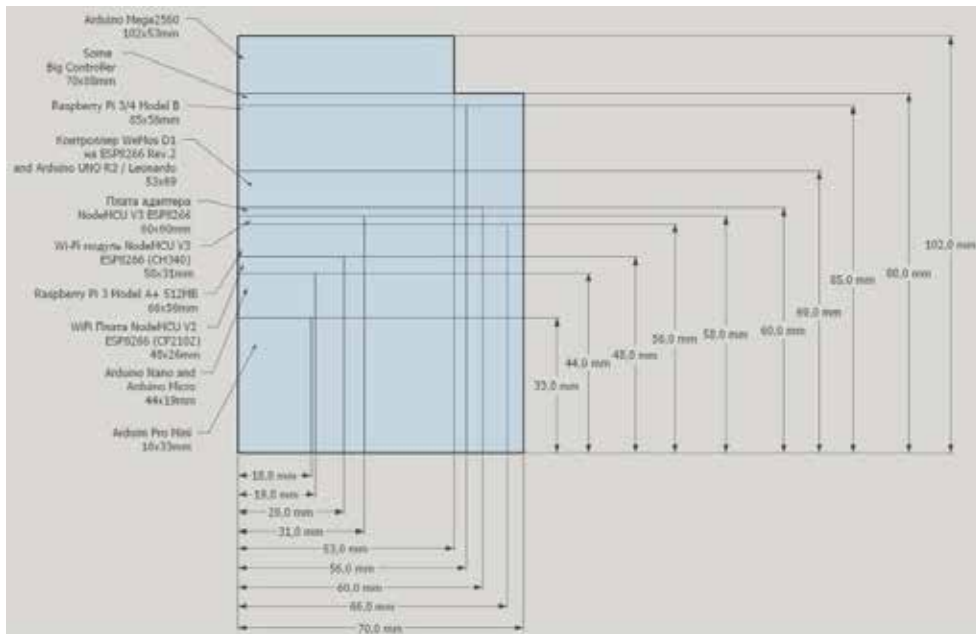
Розміри плат PCB деяких популярних модулів MCU
